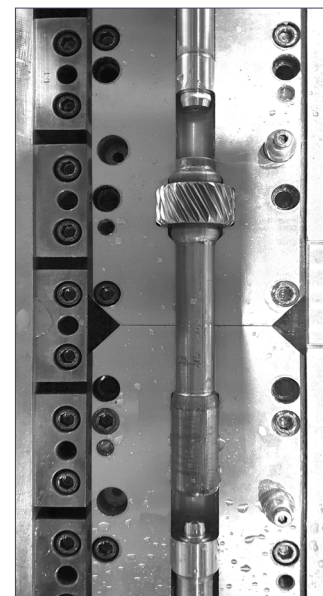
Getriebehohlwelle im IHU-Werkzeug
